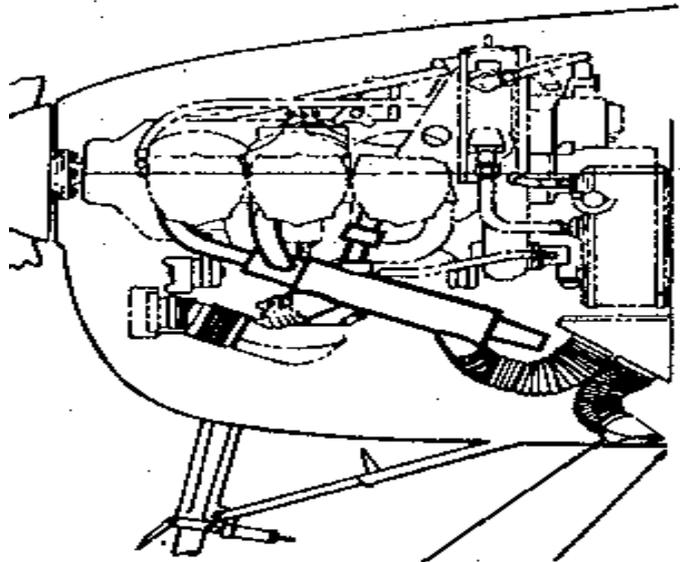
Sistema de escapamento de um motor de cilindros horizontalmente opostos.
